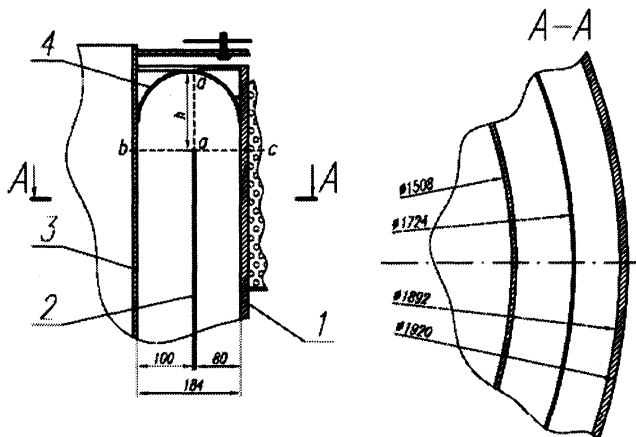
Верхняя часть рекуператора: 1 – корпус вагранки; 2 – средний (промежуточный) цилиндр; 3 – внутренний теплопринимающий корпус; 4 – направляющая
